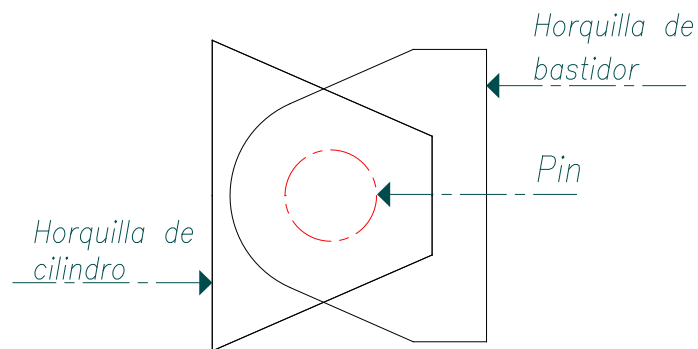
Esquema de unión entre horquilla de bastidor y horquilla de cabeza de cilindro
